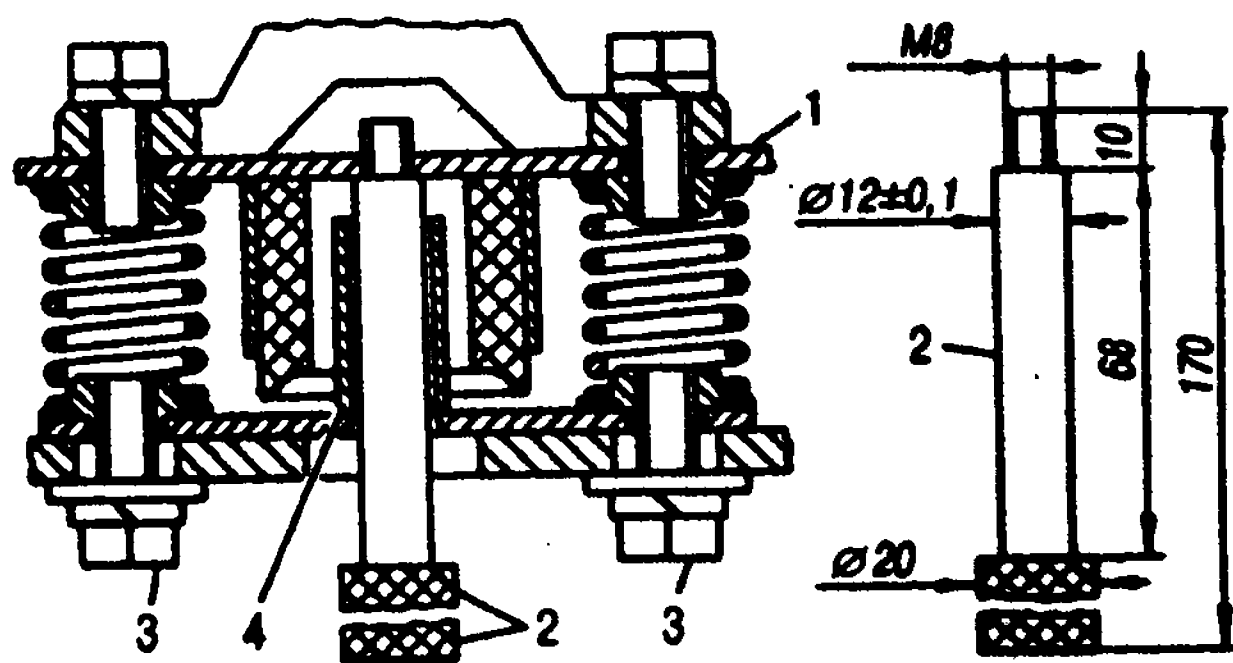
Установка задней опоры двигателя: 1 - пластина; 2 - оправка; 3 - болты; 4 - втулка
